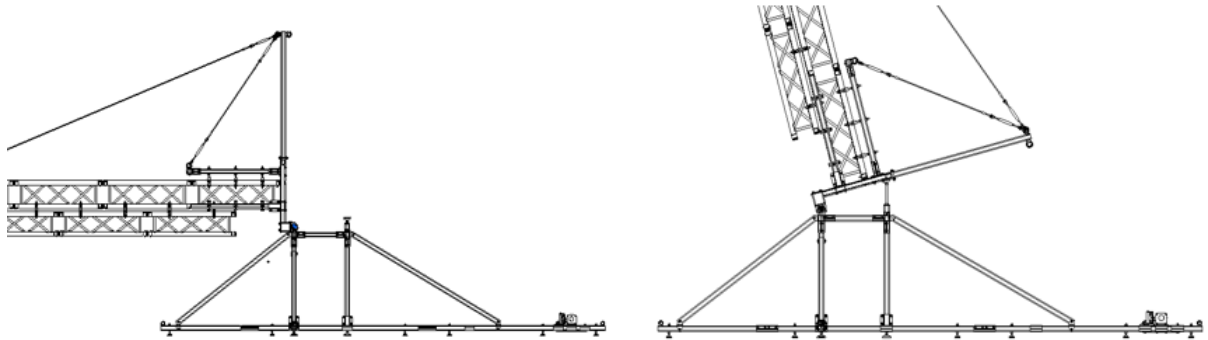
Izquierda: Posición de montaje. Derecha: Posición de lanzamiento a 15°.
